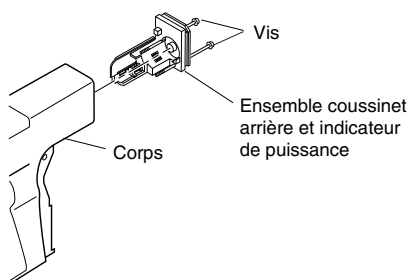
Retrait de l'ensemble tampon/indicateur de puissance de la poignée
